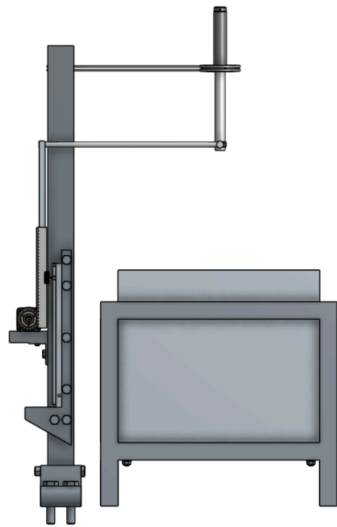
Figura XCIX. Vista frontal del ensamblaje final del diseño mecánico del movimiento axial del pasador
